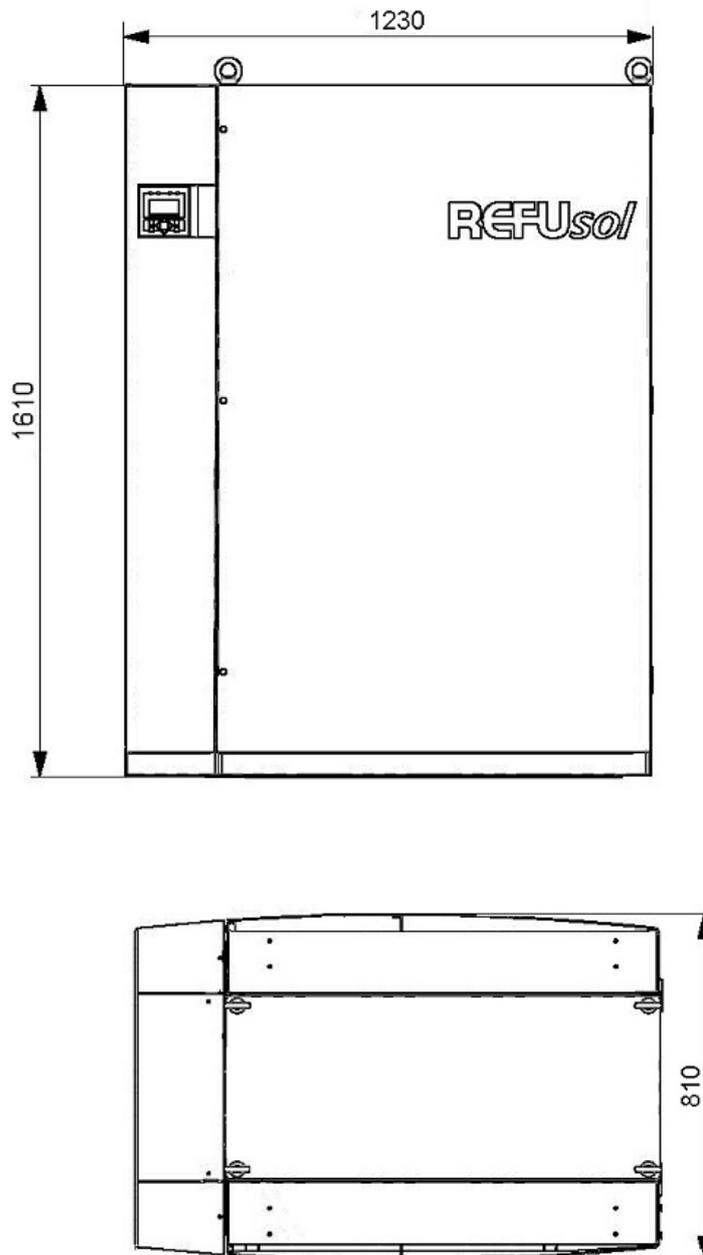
Abmessungen Solarwechselrichter REFUso/ 333K
